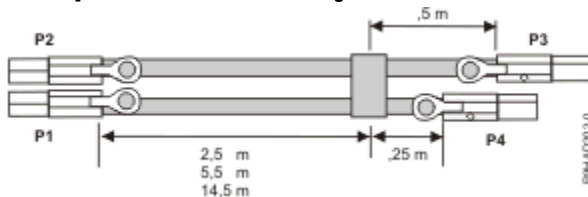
Comprimentos de cabos de montagem de cabo X externo SAS
